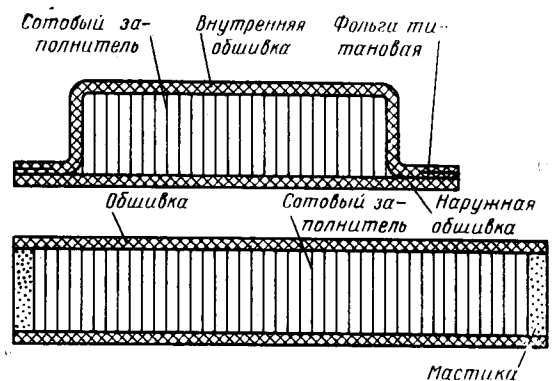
Схема детали трехслойной конструкции.
